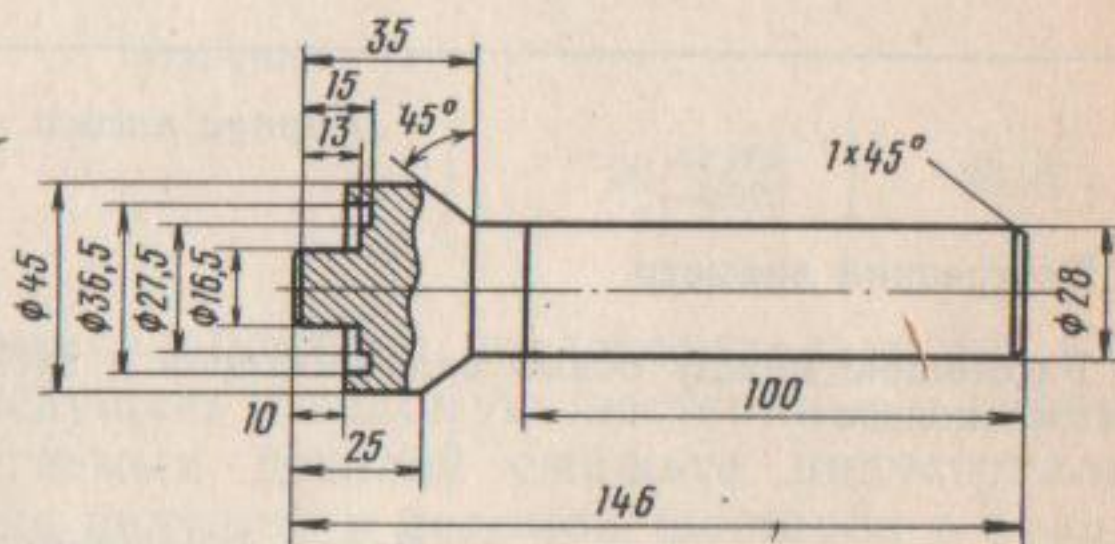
Оправка для выпрессовки и запрессовки подшипников в опору корпуса насоса рулевого управления
